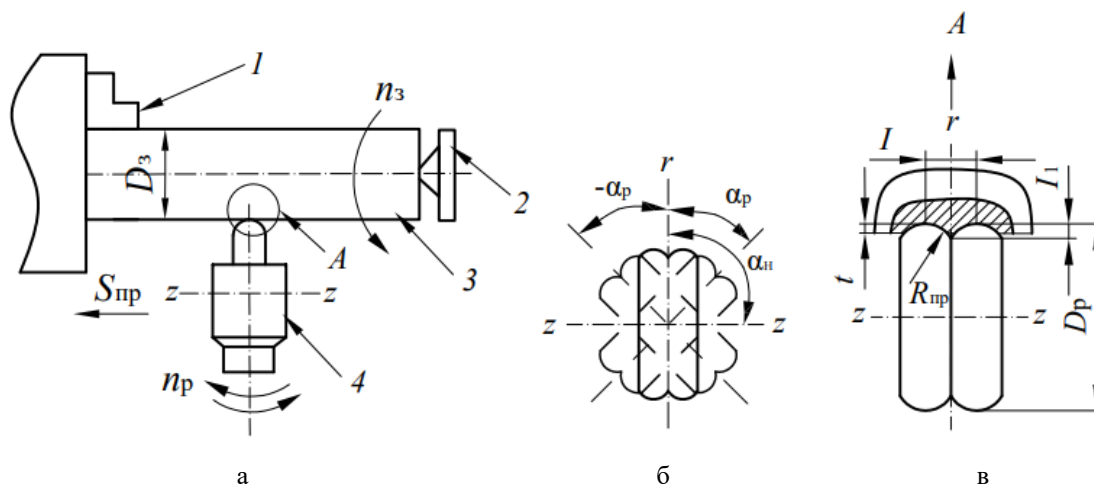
Схемы реверсивного ППД двухрадиусным роликом (а), его реверсивного вращения (б) и рабочей зоны (в) [12]: 1 – трехкулачковый патрон; 2 – задняя бабка; 3 – заготовка; 4 – рабочий инструмент
